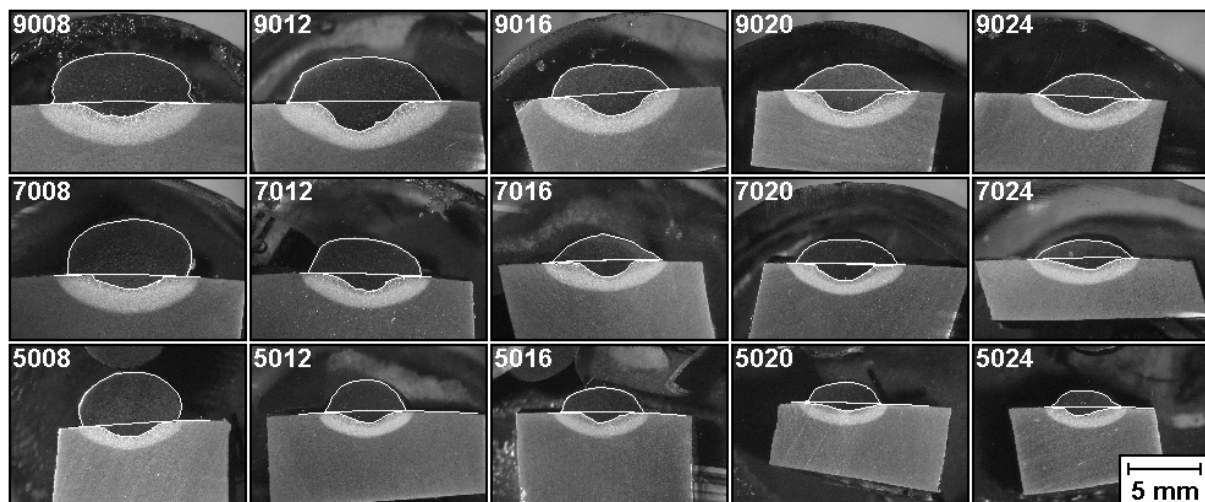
Macrografias das soldas depositadas. Linhas: mesma corrente de soldagem; colunas: mesma velocidade de soldagem. Ataque: Nital 2%.
